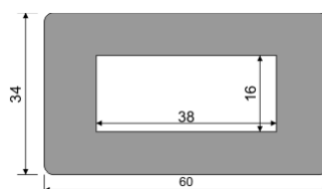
Габаритный чертеж лицевой панели FS60x34B-38x16
